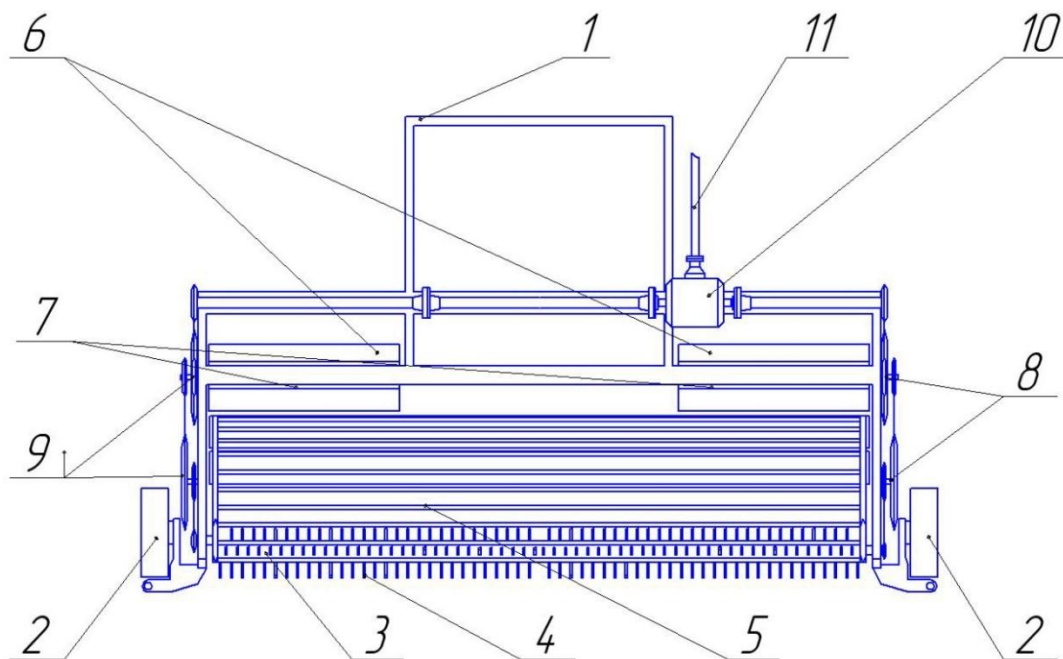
Схема кулачково-планчатого питателя (вид сверху)
